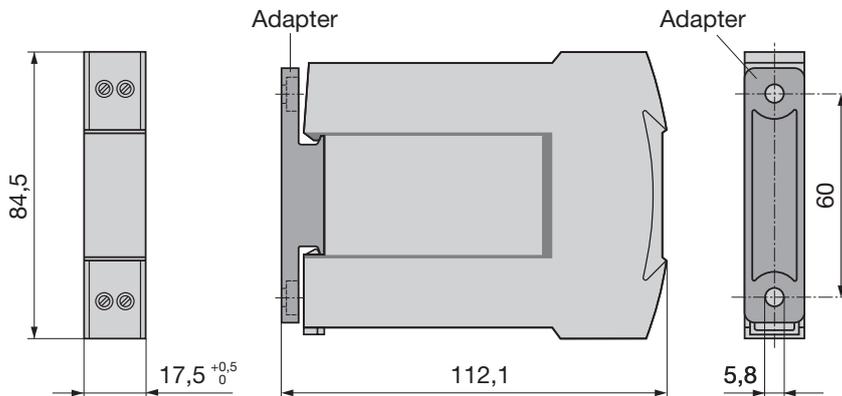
SINEAX SI 815-5.... (N17-Gehäuse) mit Adapter für direkte Wandmontage.
